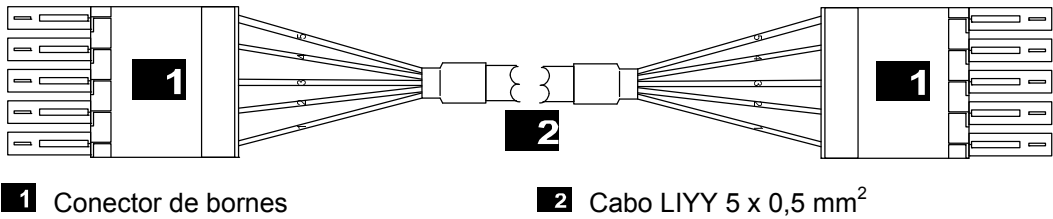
Cabo do conjunto de cabos de sistema X-CA 004 01
